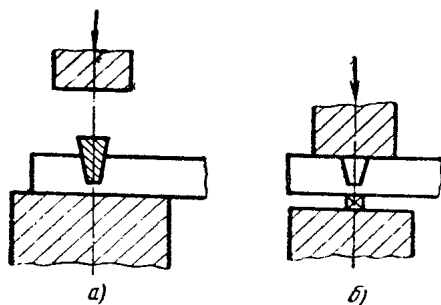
Схема разрубки под молотом с одной стороны с перемычкой:
